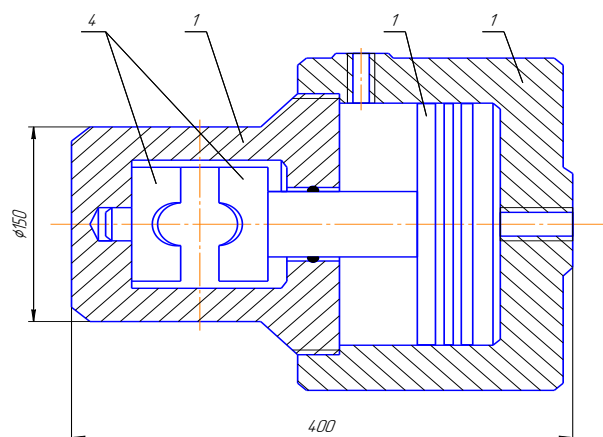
Конструктивна схема силової головки для гідравлічного преса: 1 – корпус; 2 – циліндр; 3 – поршень; 4 – профільні пуансони.
